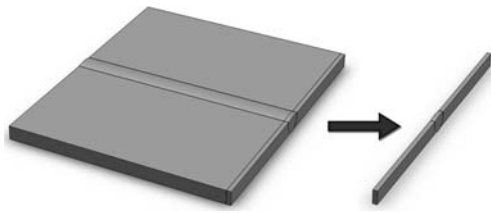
Схема вырезки плоских образцов сварного соединения из ИСС
